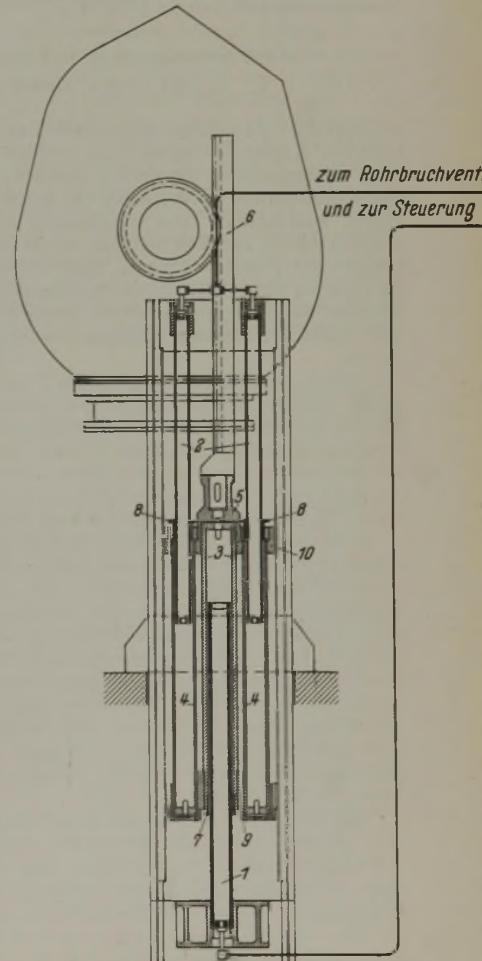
Hydraulischer Wendezylinder für einen 60-t-Konverter.
